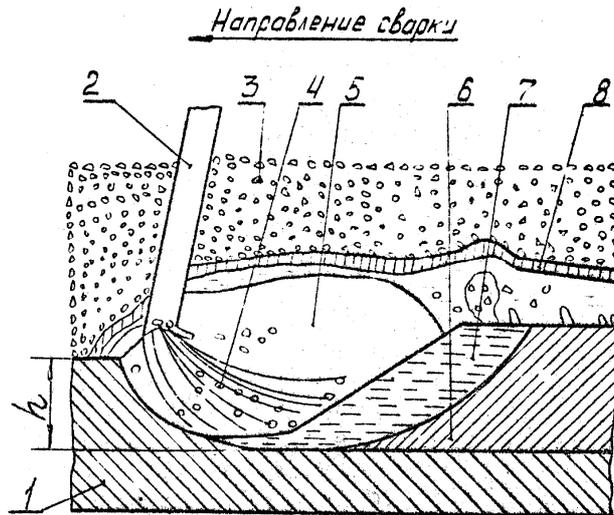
Схема процесса автоматической сварки под флюсом:
